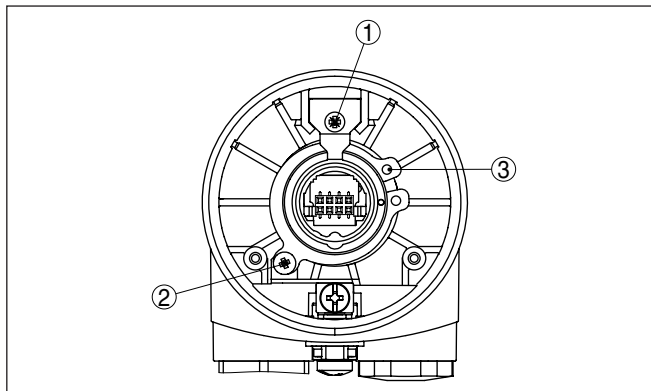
Положение винтов и стопорного кольца, например, на пластиковом корпусе
